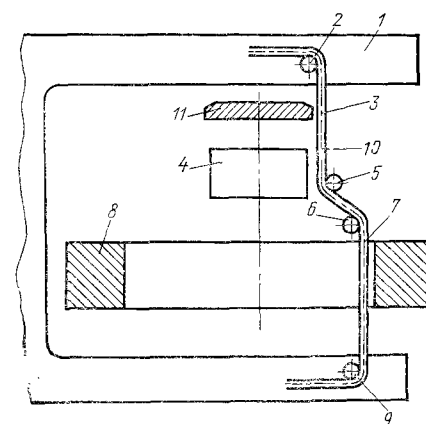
Одновременная обработка фасонных поверхностей непрерывно движущейся электрод-проволокой
